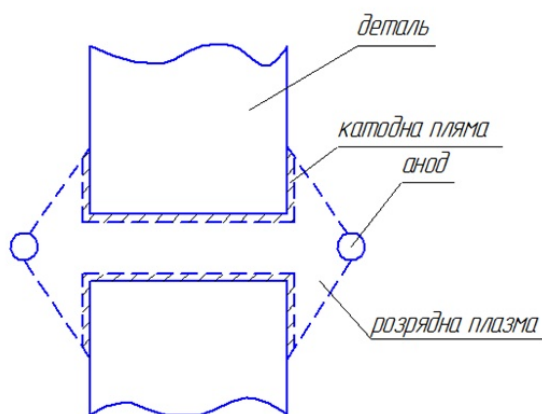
Схема іонної обробки зварюваних поверхонь металів
